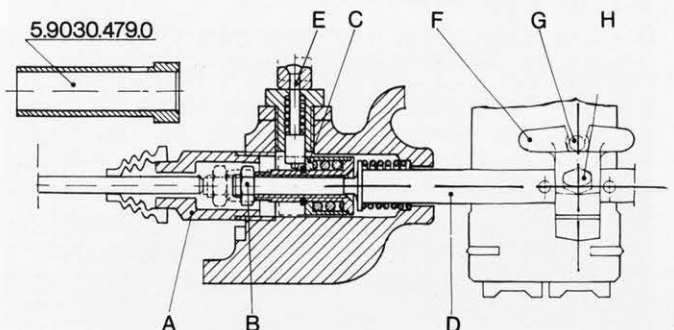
Verbindung Einspritzpumpe - Regler.
